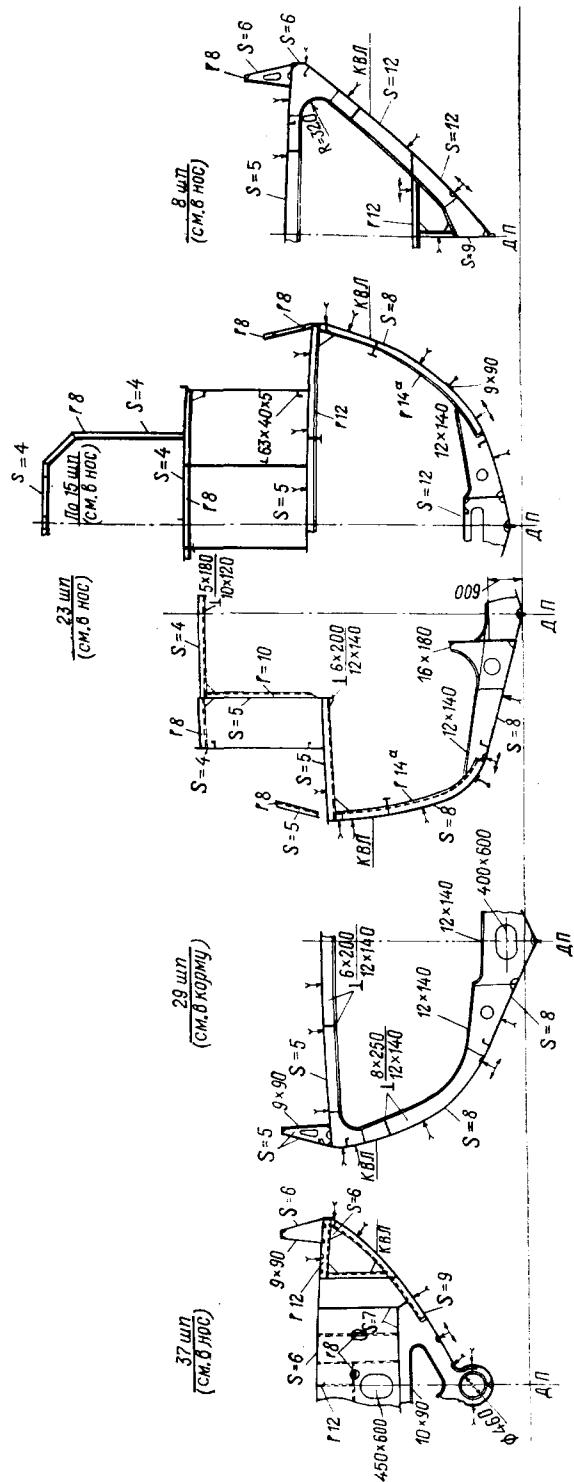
Конструктивные сечения корпуса буксира Рейд.
